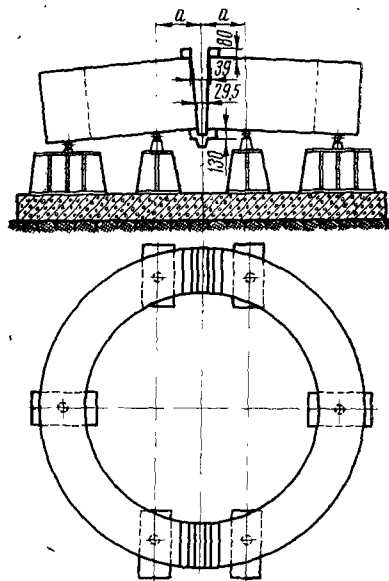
Сборка половины бандажа под сварку
